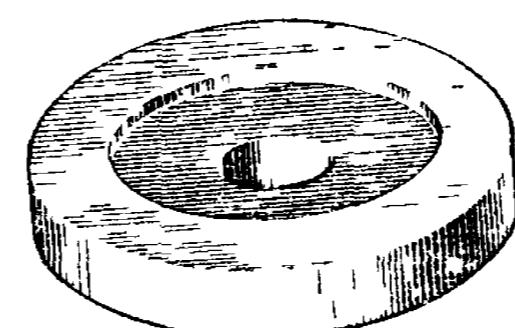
Кольцо к оправке (см. рис. 30) для демонтажа переднего корпуса из картера двигателя
